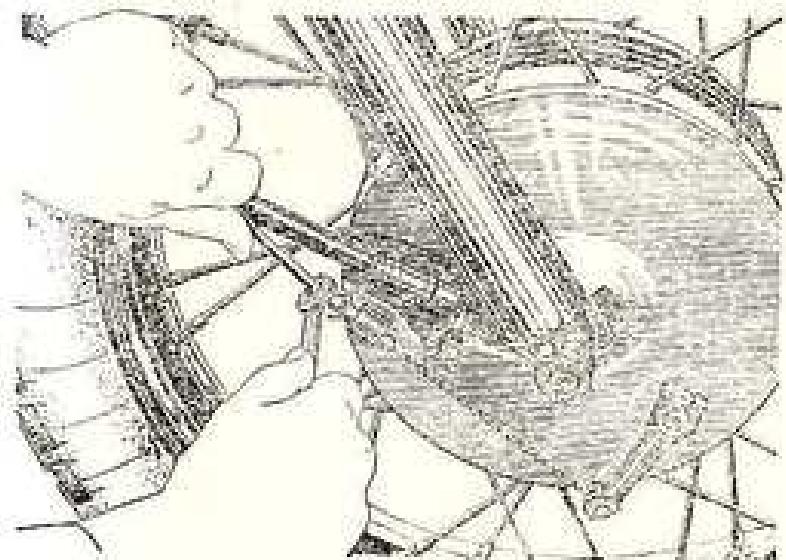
РЕГУЛИРОВКА РУЧНОГО ТОРМОЗА
